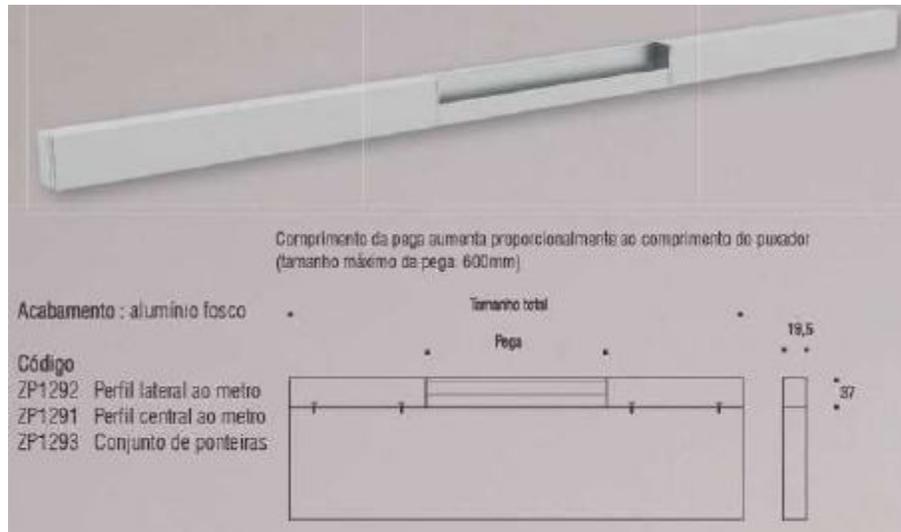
CROQUI DA MONTAGEM DO PUXADOR TIPO PERFIL LINEAR PRETENDIDO
